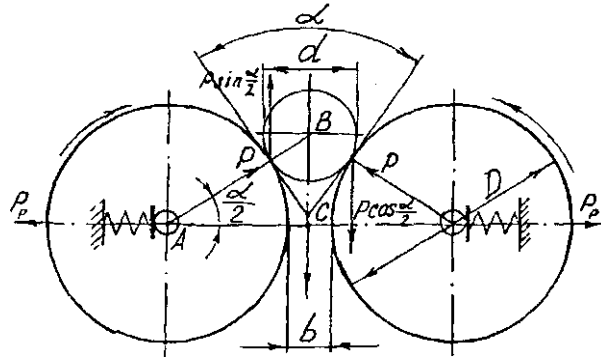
Розрахункова схема вальцевої дробарки.
